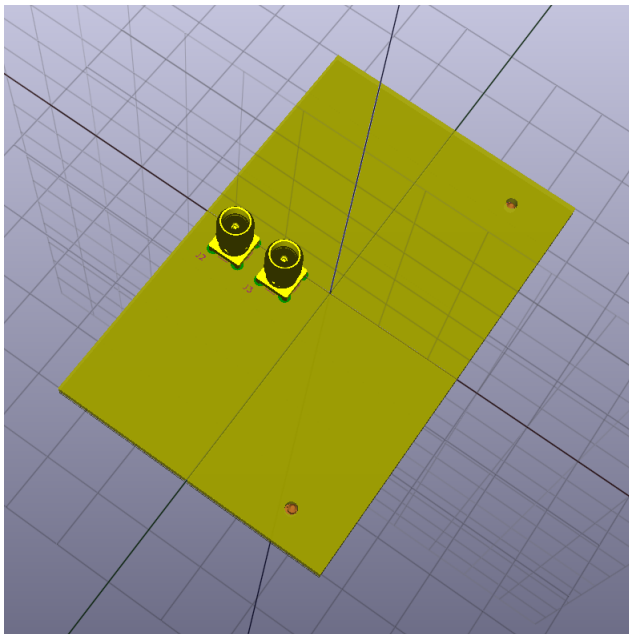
Vista frontal de la PCB fabricada. *Modelo 3D extraído de KiCad.
